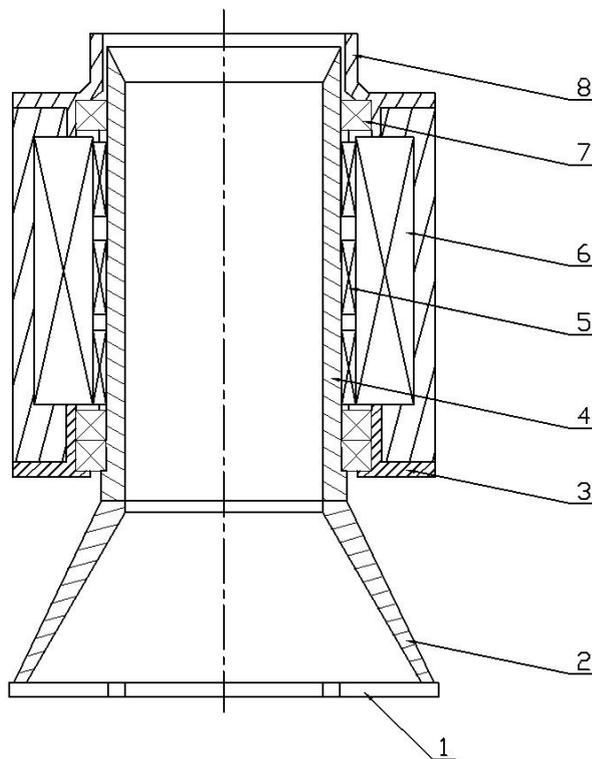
Схема торцевой фрезы-электродвигателя: 1 - ножи, 2 - ножевая головка, 3- передняя крышка электродвигателя, 4-ротор, 5-постоянные магниты, 6-статор, 7- подшипник качения, 8-задняя крышка электродвигателя со стружкоотводом
